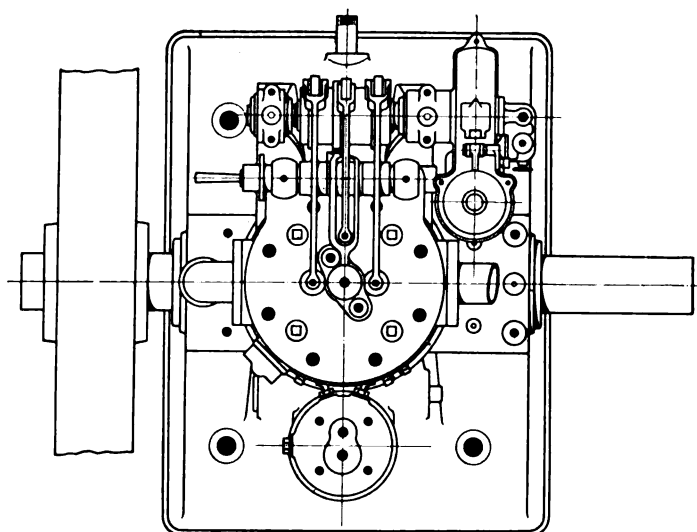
die Brennstoffpumpe einer dreizylindrigen Maschine; sie besitzt selbst drei kleine Pumpzylinder, einen für jeden Kraftzylinder. Der Regulator steht in Verbindung mit drei Rücklaufventilen, welche er während des Druckhubes mehr oder weniger lange offenhält; erst wenn diese Ventile jeweils geschlossen sind, tritt der Brennstoff durch die eigentlichen Druckventile in die Düse über. Die Pumpe wird ebenfalls von der im Gestellkasten befindlichen wagerechten Steuerwelle angetrieben.
